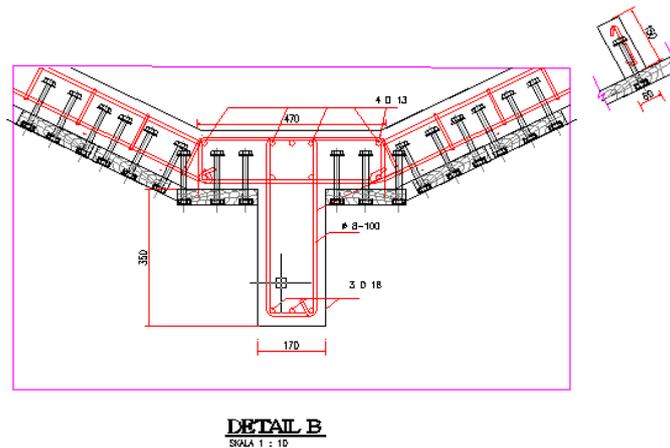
DETAIL II = SAMBUNGAN LUNAS BETON DAN KAYU PADA LINGGI HALUAN + PAPAN LAMBUNG
